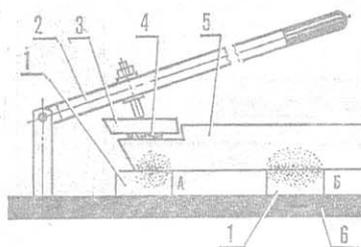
Контактный участок аппарата: 1 — контактные шины (красная медь), 2 — прижимной рычаг, 3 — твердосплавная пластина, 4 — припой, 5 — державка резца, 6 — изолятор основания; А и Б — зоны нагрева.
